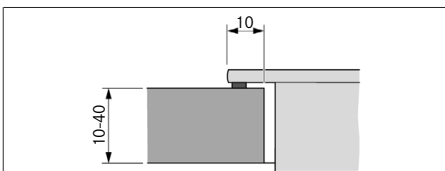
Rozmery drážky pre zapustenú montáž
